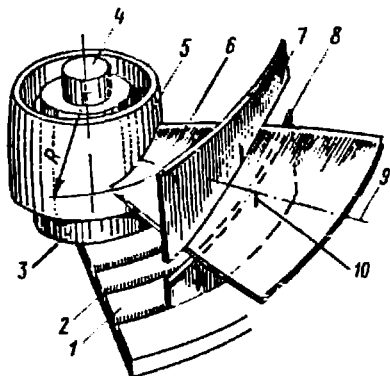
Схема приспособления для сборки ротора и обработки лопастей.
